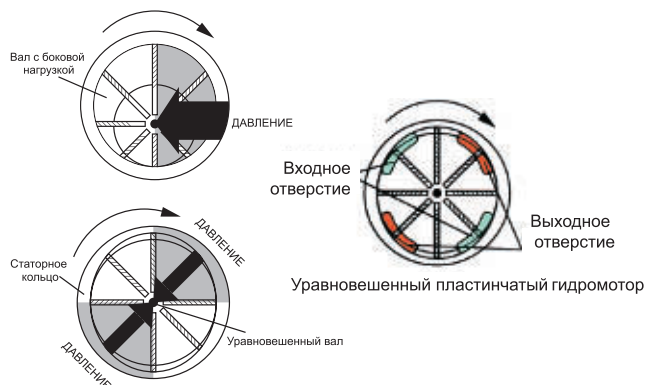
Сбалансированный пластинчатый гидромотор
